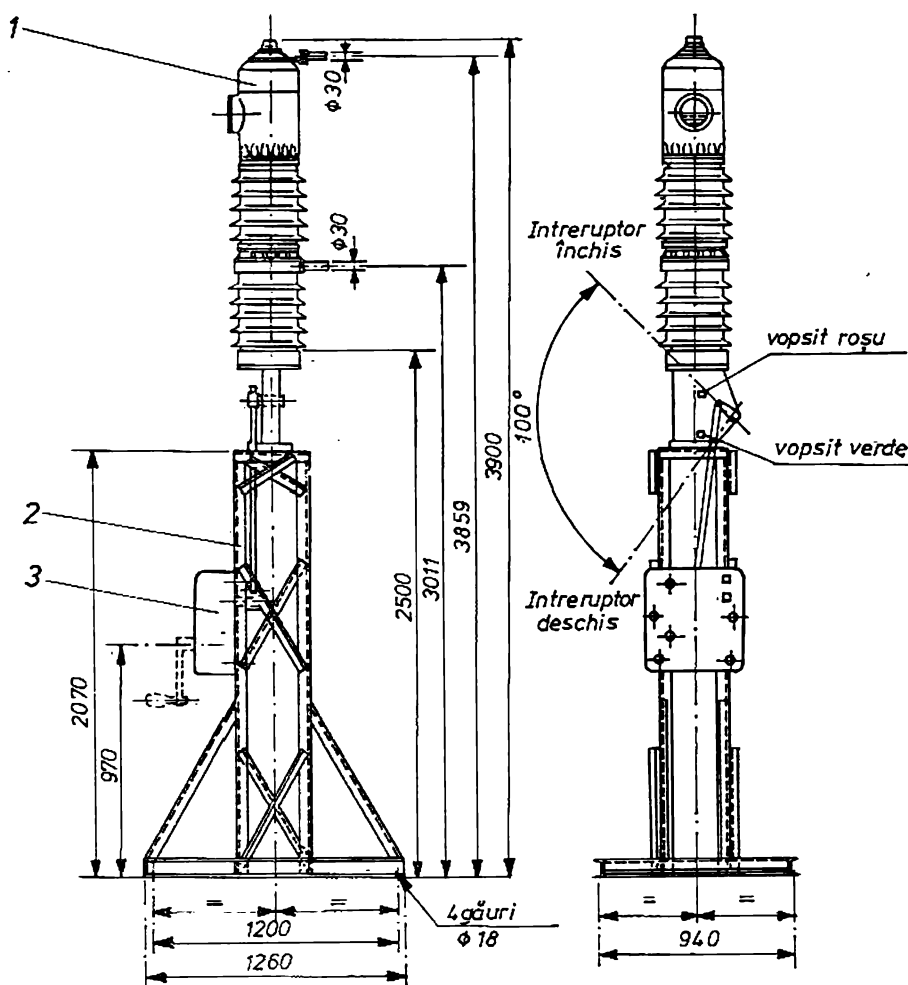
Înteruptoare IUP 25/1250. Dimensiuni de gabarit :
